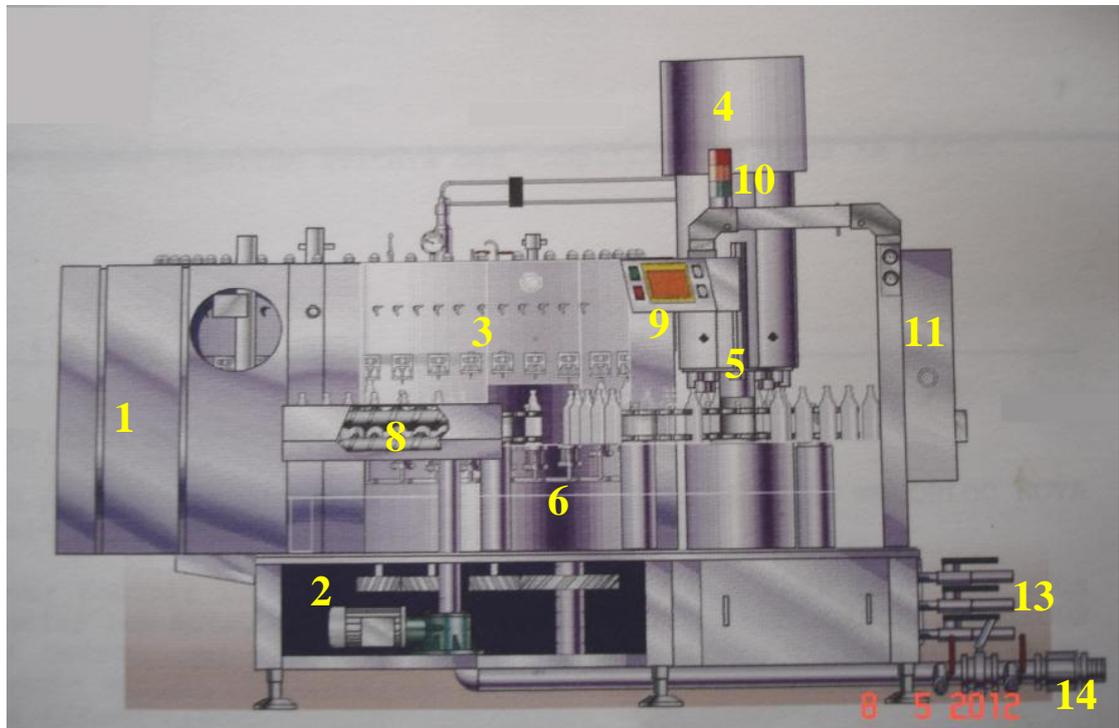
Vue face de la remplisseuse MONOBLOC [10].
